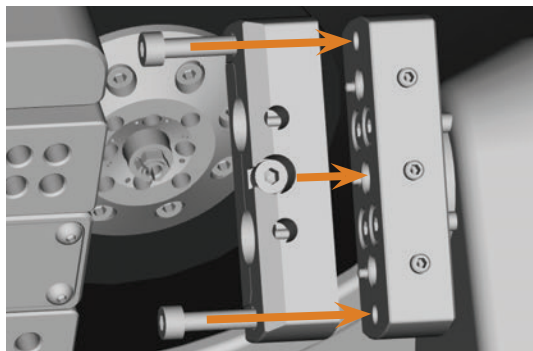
COLOCACIÓN DEL SOPORTE DE PILARES PREFACE®
